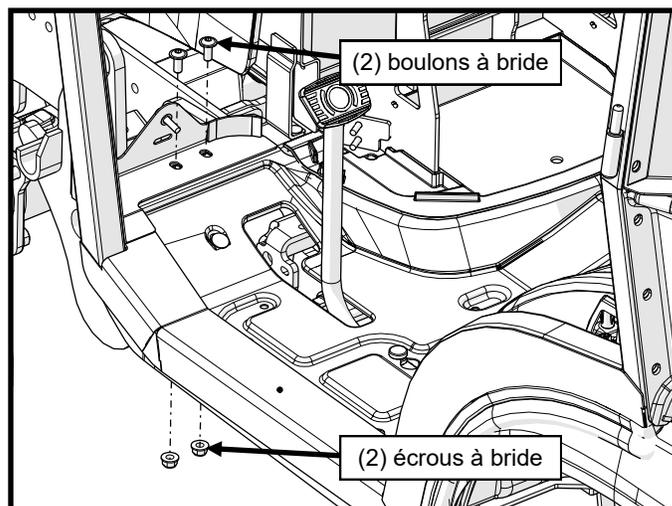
Fixation de l'avant du cadre latéral au plancher
